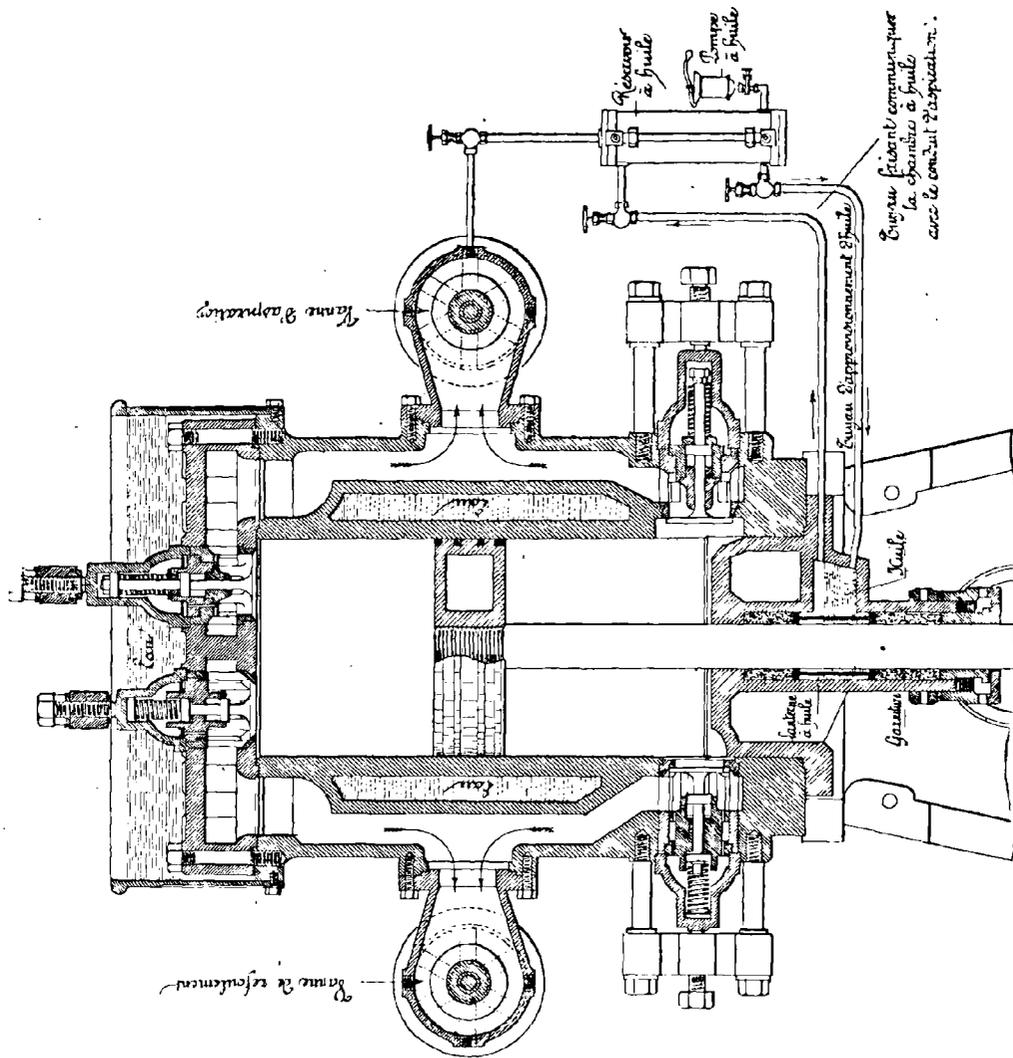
Compresseur de la Buffalo Refrigerating Machine C.
